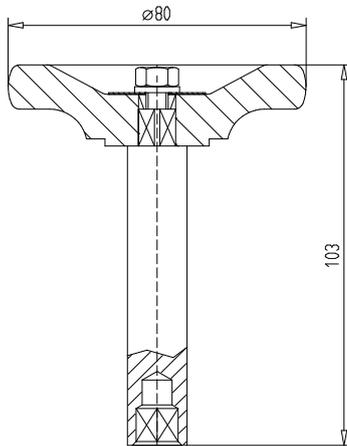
Handrad-Steckschlüssel PAW 6695.0808
